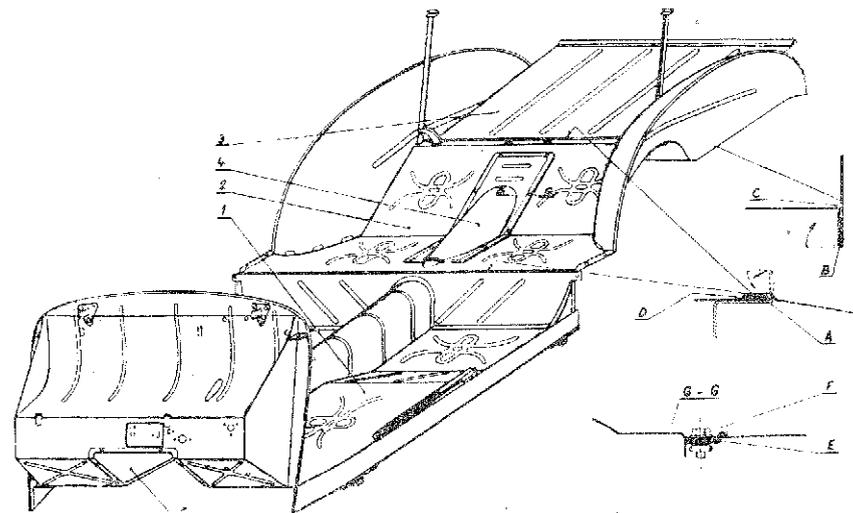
Demontáž karoserie ze chassis Š 1101, 1102
